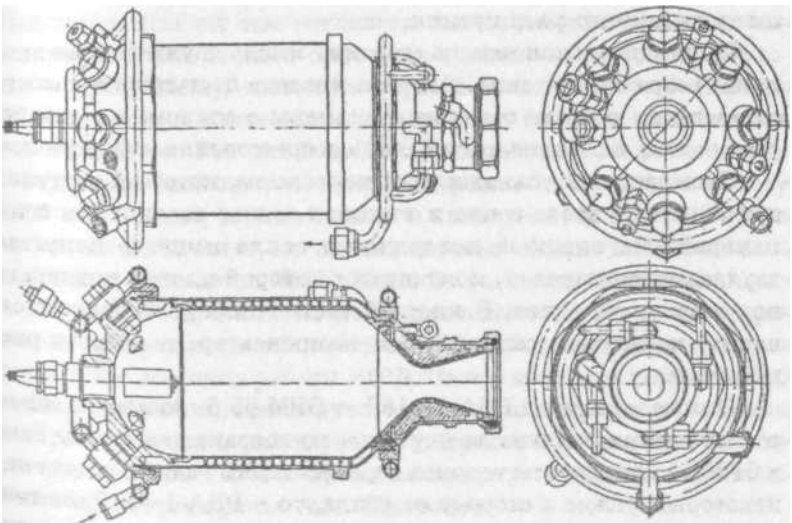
Жидкостный ракетный двигатель РДА-1 —150 [12]
